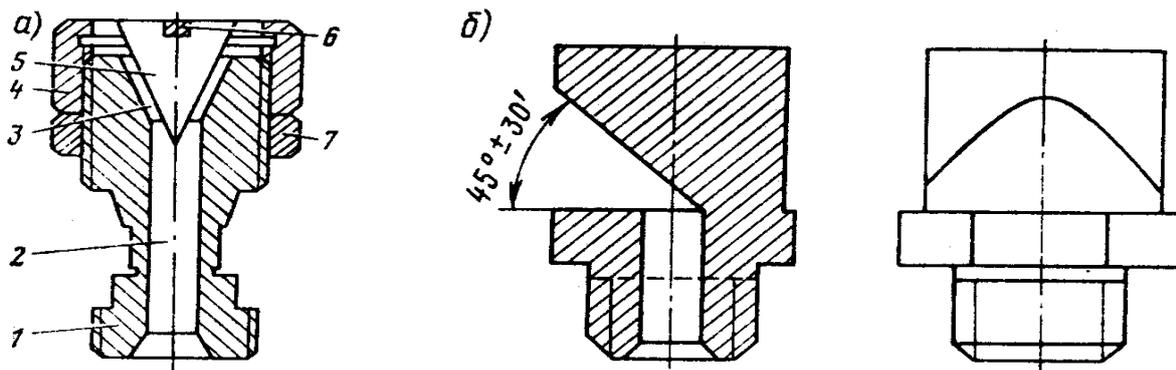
Типы форсунок для струйных моечных установок: а-регулируемый; б-нерегулируемый с боковым впрыском; 1-корпус; 2-канал проходной; 3- конусное кольцо отверстия; 4-гайка; 5-вращающихся конус; 6-пробка; 7-гайка ограничительная.
